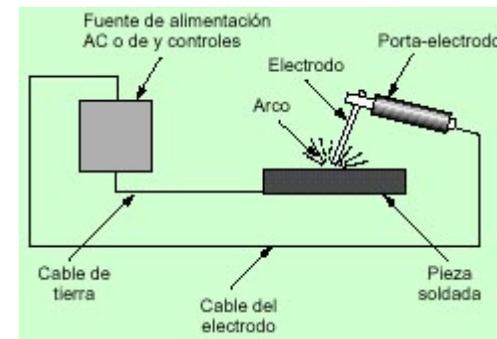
Esquema del proceso de soldadura eléctrica al arco
